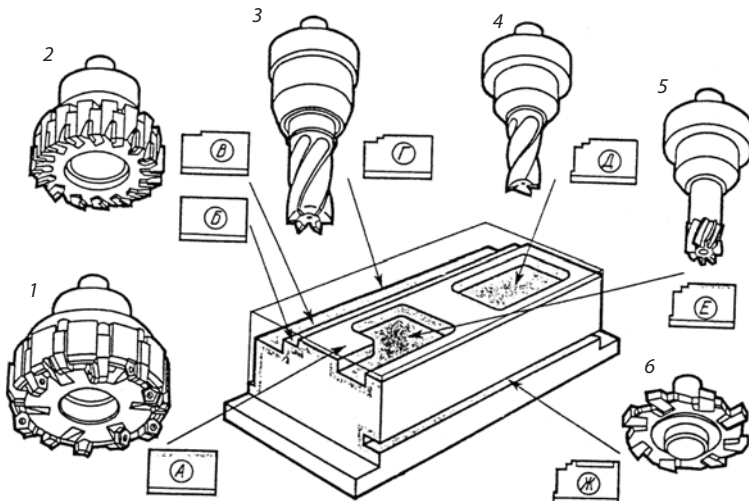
Зоны обработки детали типа «корпус»: 1–6 — применяемый инструмент
